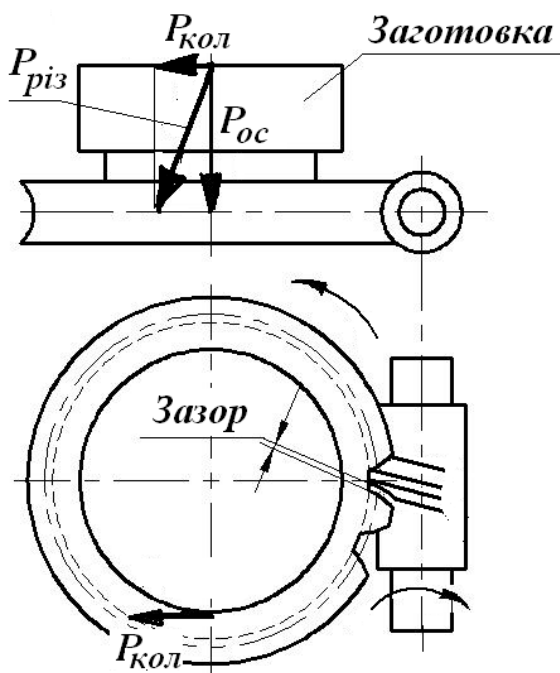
Схема сил різання і впливу бокового зазору при обробці косозубих коліс
